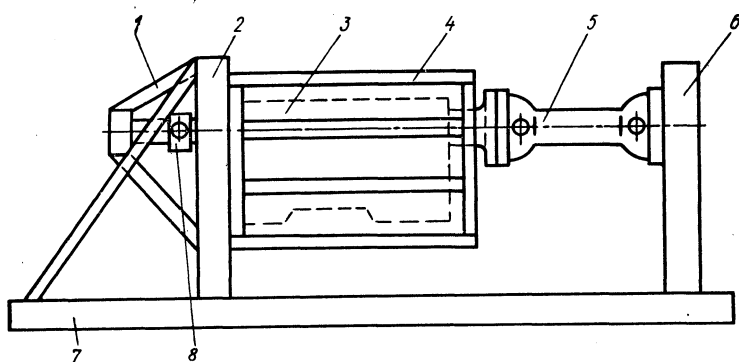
Схема стана для испытания коробок передач на жесткость: 1 — опора первичного вала; 2 — передняя стойка; 3 — испытываемая коробка; 4 — каркас; 5 — карданная передача; 6 — задняя стойка; 7 — основание; 8 — нагрузочное устройство
